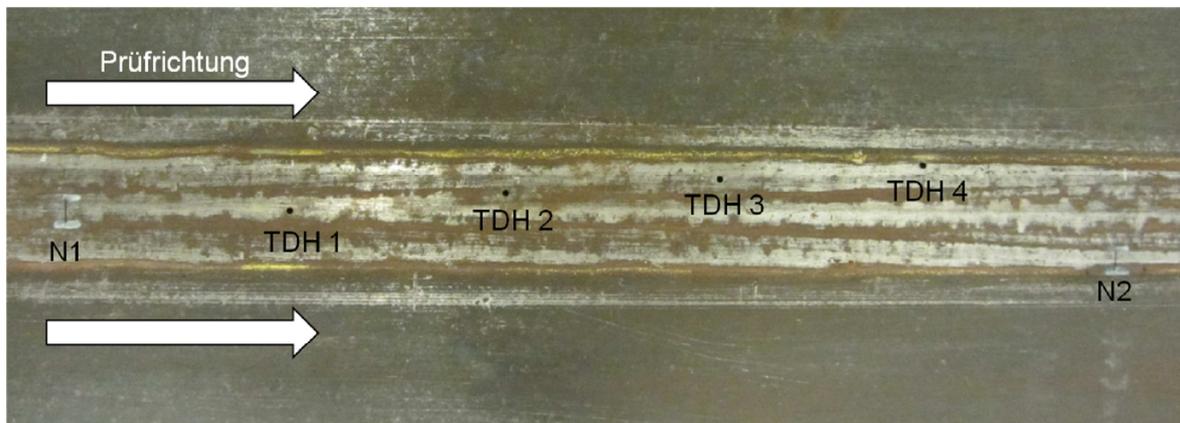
In die Schweißnaht eingebrachte Referenzfehler
